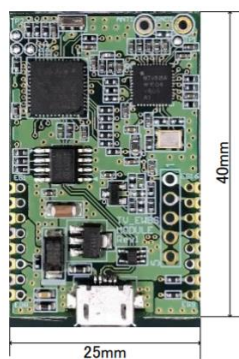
Dimensiones de Módulo Sintonizador EWBS-Superimpose
